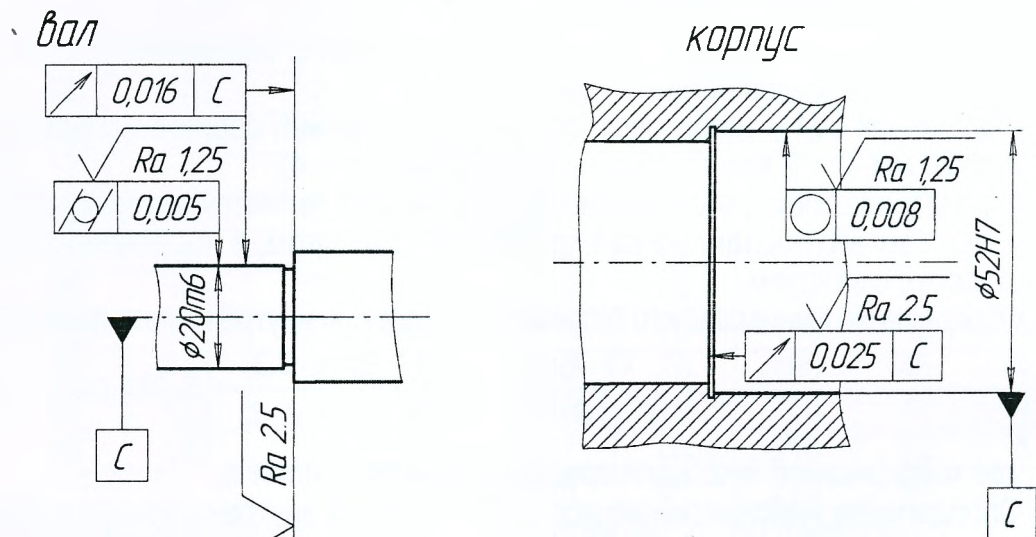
Эскизы сопрягаемых деталей и сборочного узла ПК
